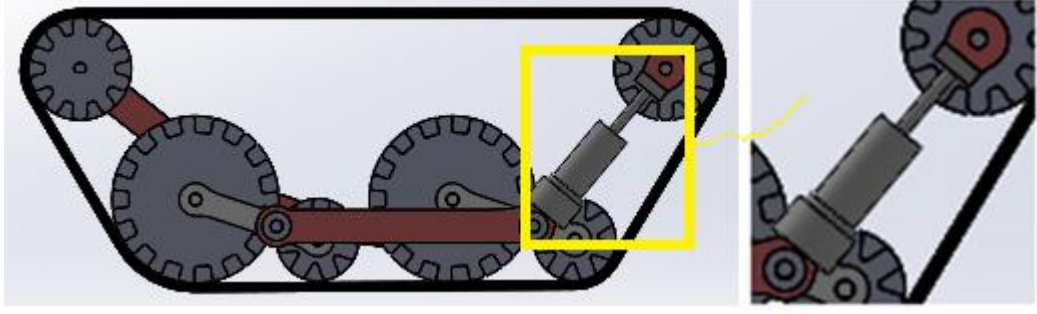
Robot mekanik tasarımı soldan görünüş
